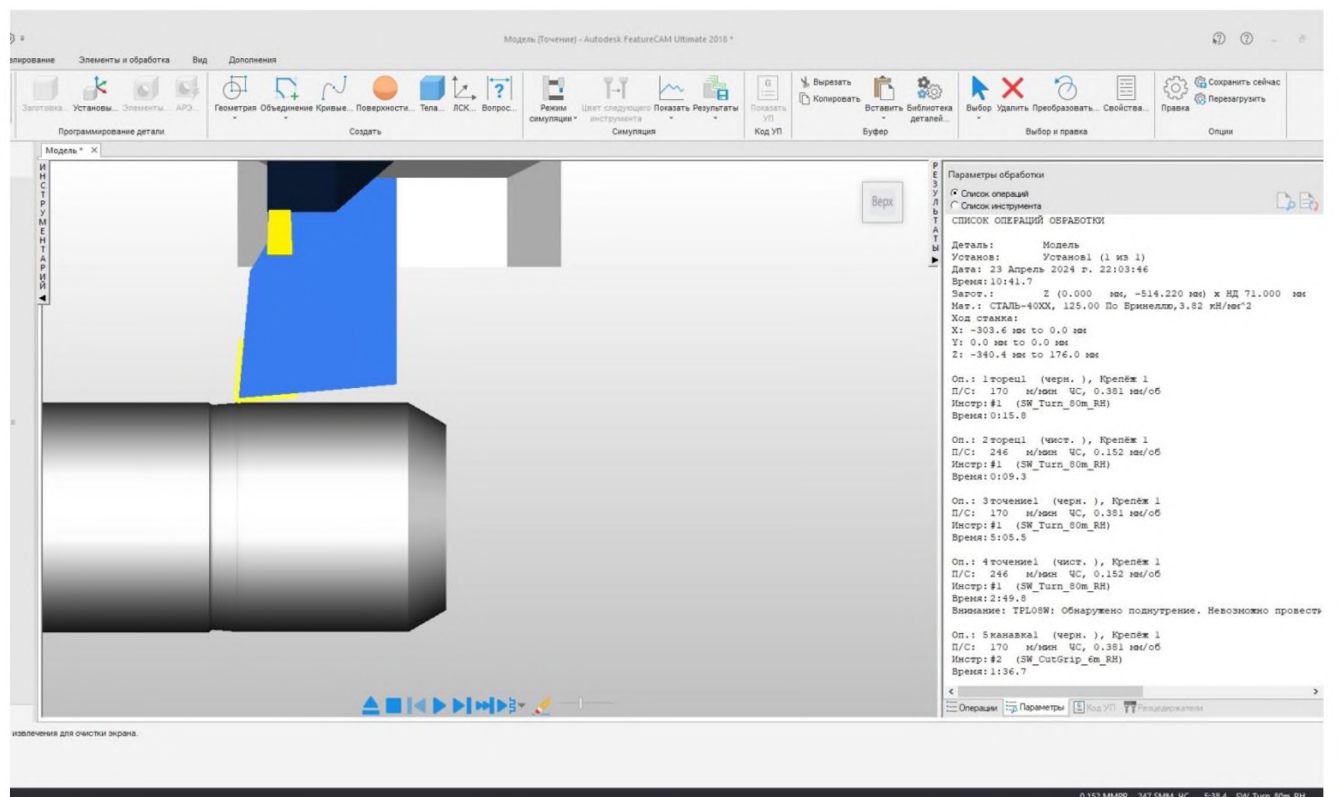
Моделювання процесу обробки деталі «Вал шліцьовий» – точіння (чистове) циліндричної поверхні
